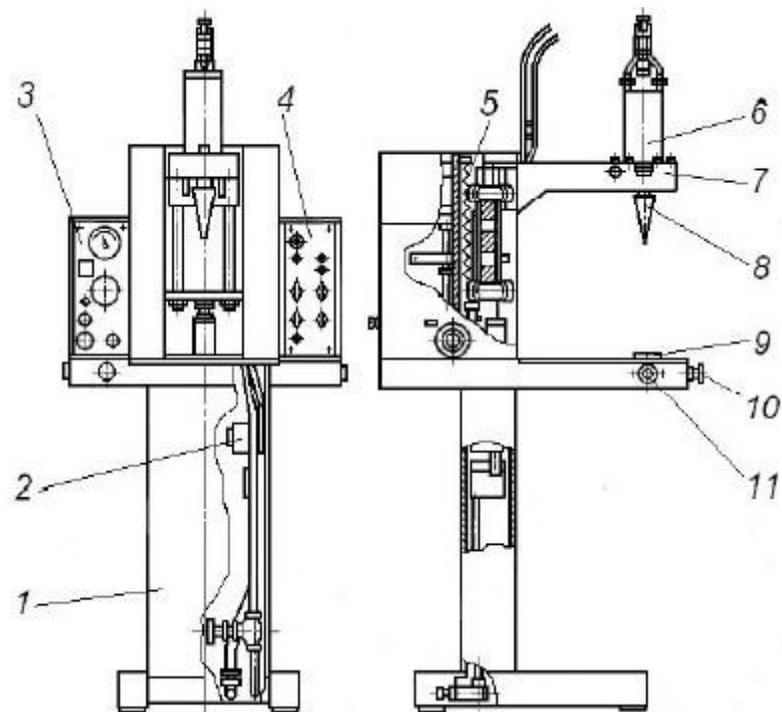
Конструктивная схема сварочной машины МТУ-1,5-3У4: 1 – стойка; 2 – реле давления воды; 3 – регулятор давления; 4 – регулятор цикла сварки; 5 – пружина; 6 – сварочный узел; 7 – кронштейн; 8 – волновод; 9 – опора; 10 – кнопка аварийного отключения; 11 – кнопка включения
